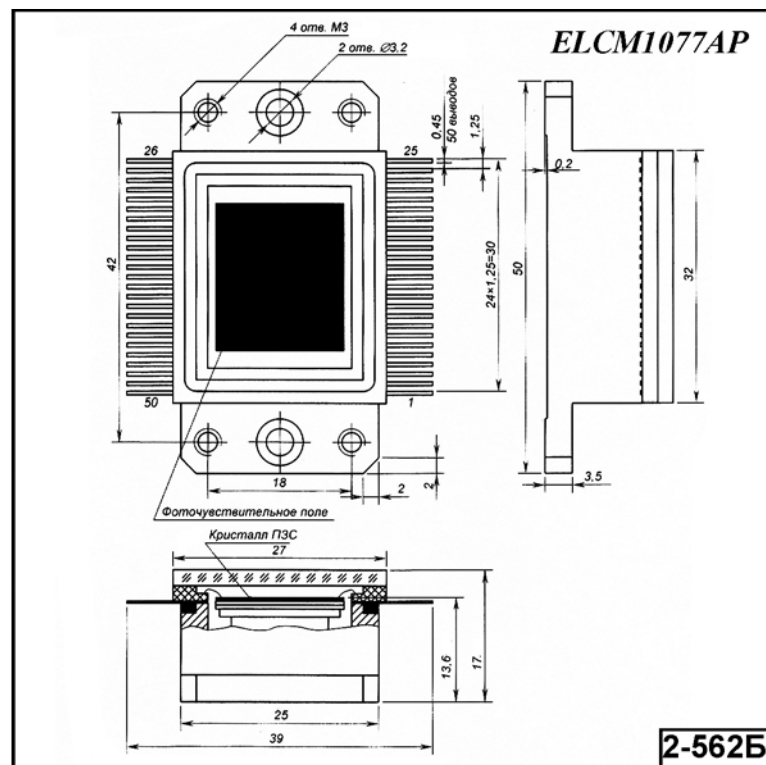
Внешний вид и габаритные размеры ФПЗС ELCM1077AP
